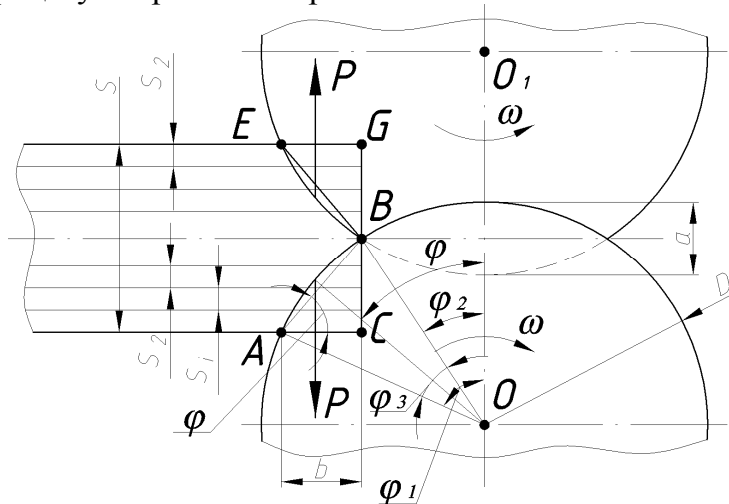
Розрахункова схема для визначення зусилля різання багат шарової гладкої конвеєрної стрічки дисковими ножами
